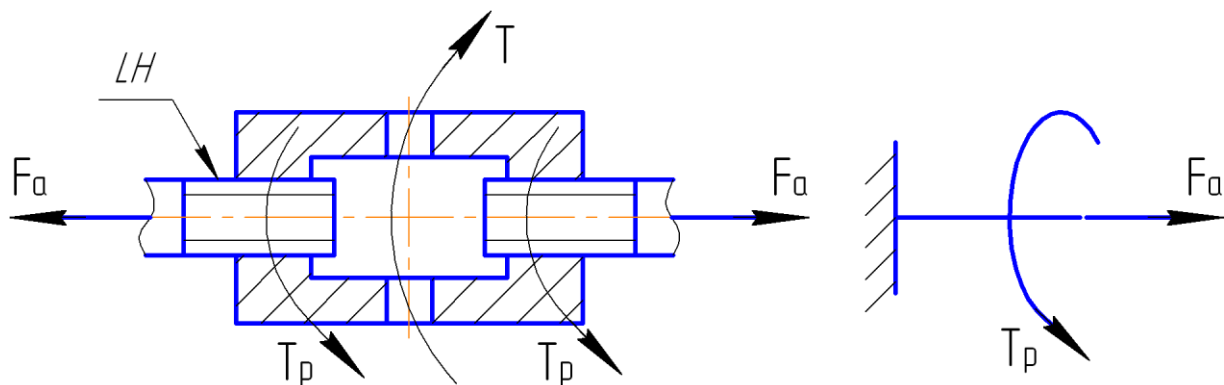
Гвинтова стяжка і розрахункова схема гвинта
